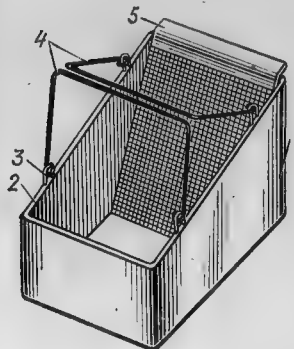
1 — корпус; 2 — отбортовка; 3 — пружина; 4 — ручки; 5 — сетка
